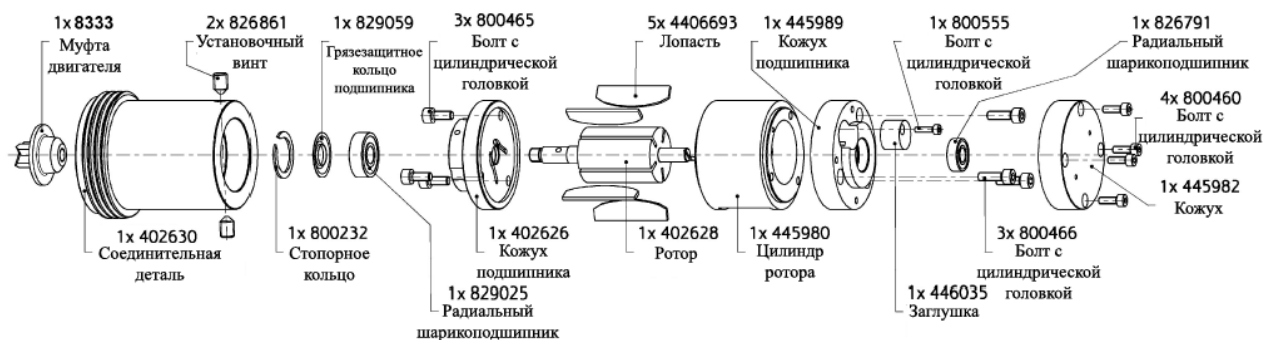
Детализовка пневматического двигателя JP-AIR 1.
